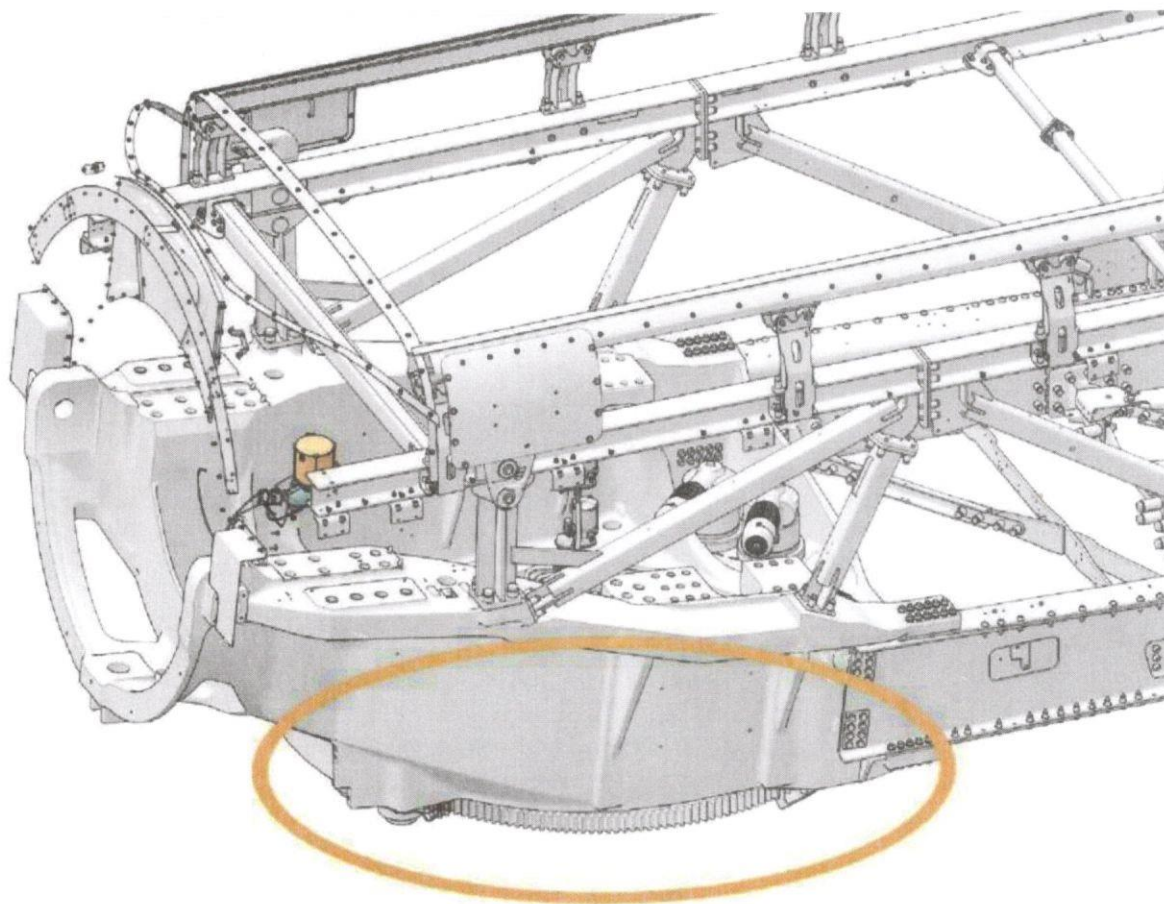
Wyrównanie potencjałów pierścienia gondoli
